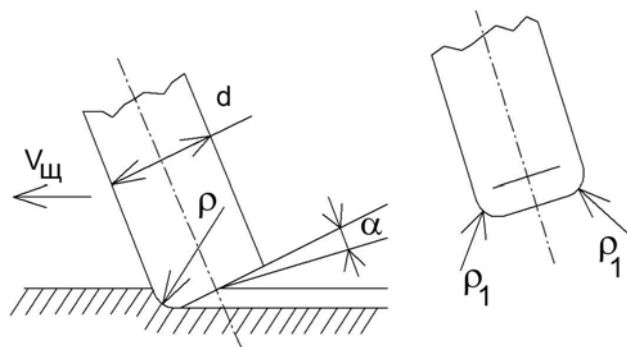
Дійсна форма робочої поверхні одиничного елемента.
